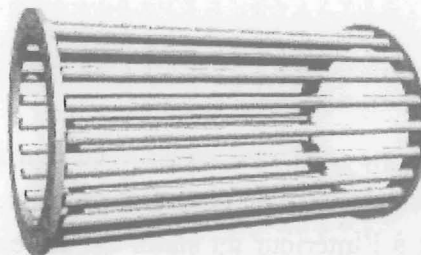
Rotor de machine asynchrone en cage d'écureuil
